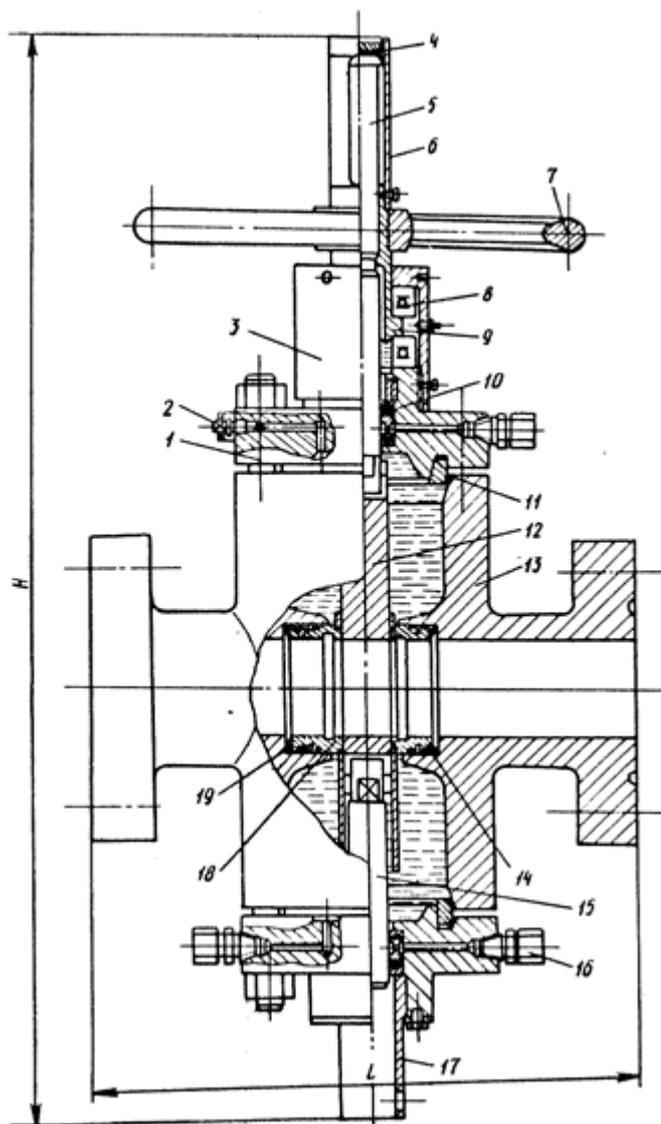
Задвижки типов ЗМС и ЗМСІ с ручным приводом:
